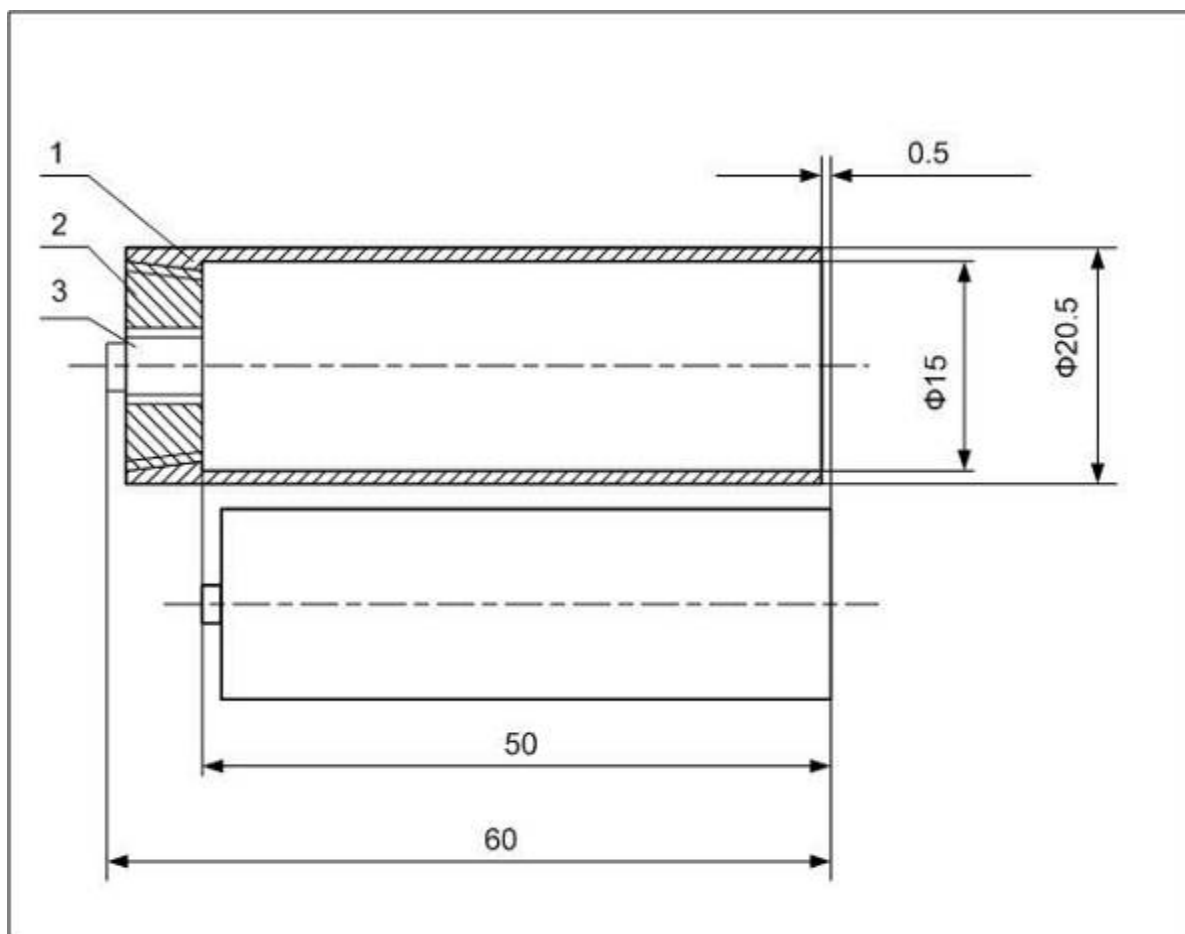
Чертеж для изготовления переходников из форм-фактора АА (316) в КБ-1
